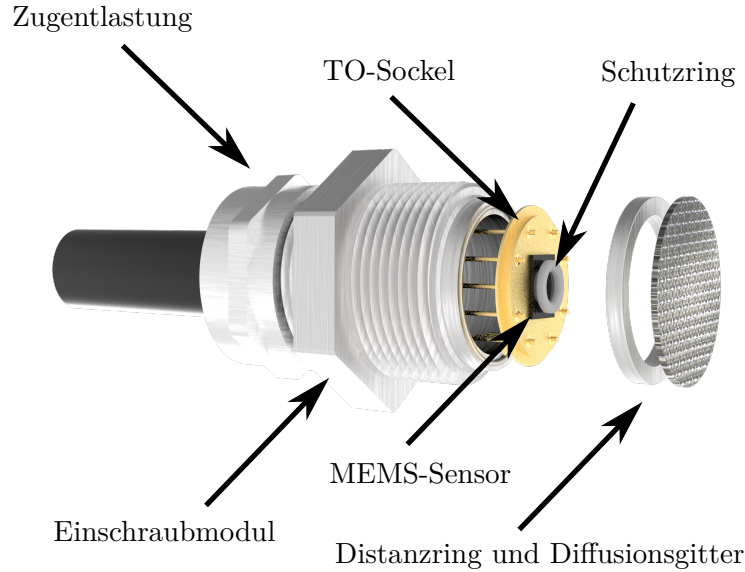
Explosionszeichnung des MEMS-Sensor Packages.
